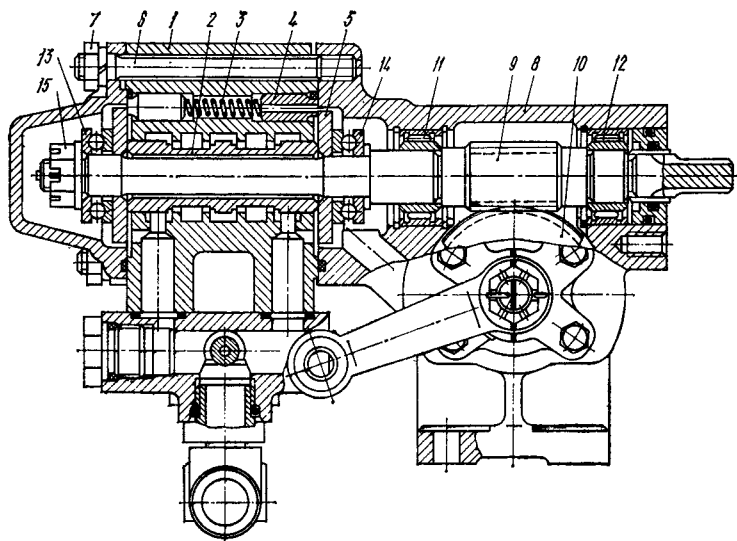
Распределитель гидросистемы рулевого управления трактора К-701 с редуктором:
